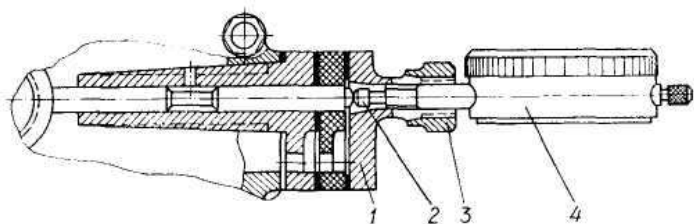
Приспособление для замера выступания штанги привода топливного насоса:
